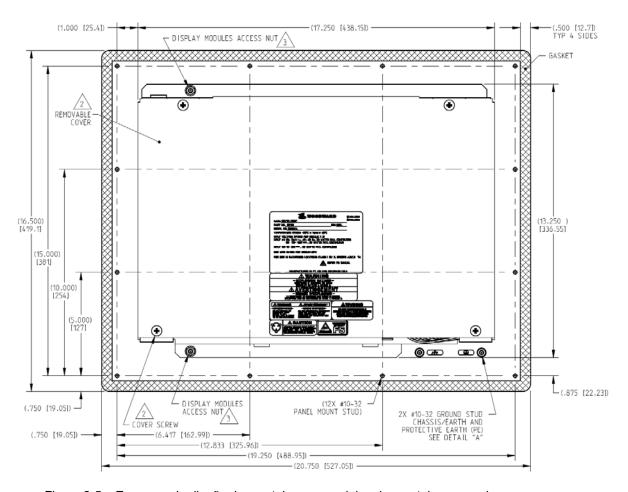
Esquema de diseño de montaje para modelos de montaje en panel
